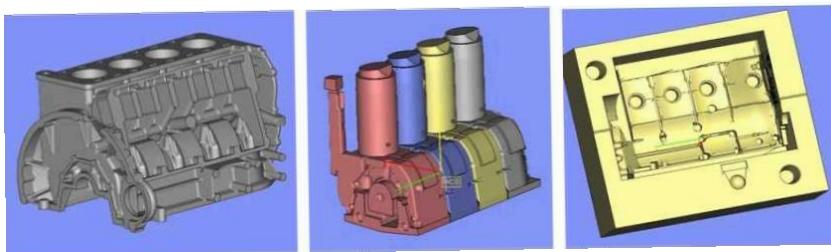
САD-модели блока цилиндров и фрагментов песчаной формы для его отливки
